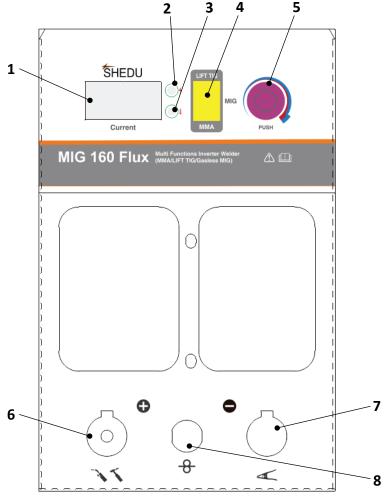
Инверторный сварочный аппарат. Основные элементы.
